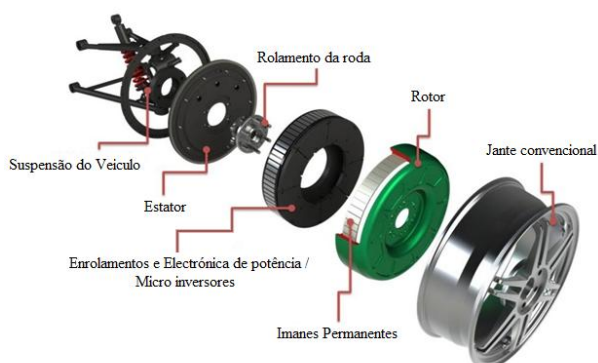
Sistema de motor eléctrico acoplado na roda (In-Wheel) [63]
